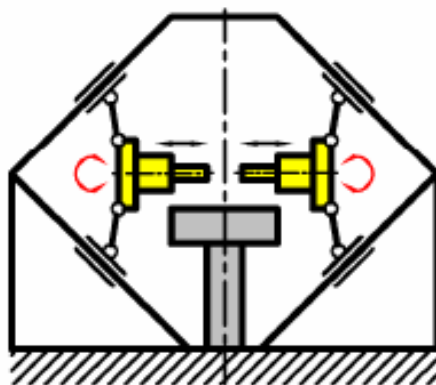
Принципиальная схема станка-робота для обработки зубчатых колес
